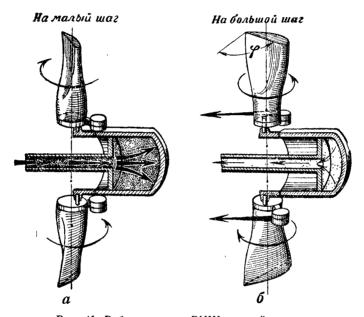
Работа втулки ВИШ прямой схемы. а-под давленчем поступающего масла подвижный цилинар двигается вправо и поворачивает лопасть на малый шаг; 6-противовес под действием центробежной силы поворачивает лопасть на большой шаг; цилиндр двигается влево и выжимает масло из своей полости.
